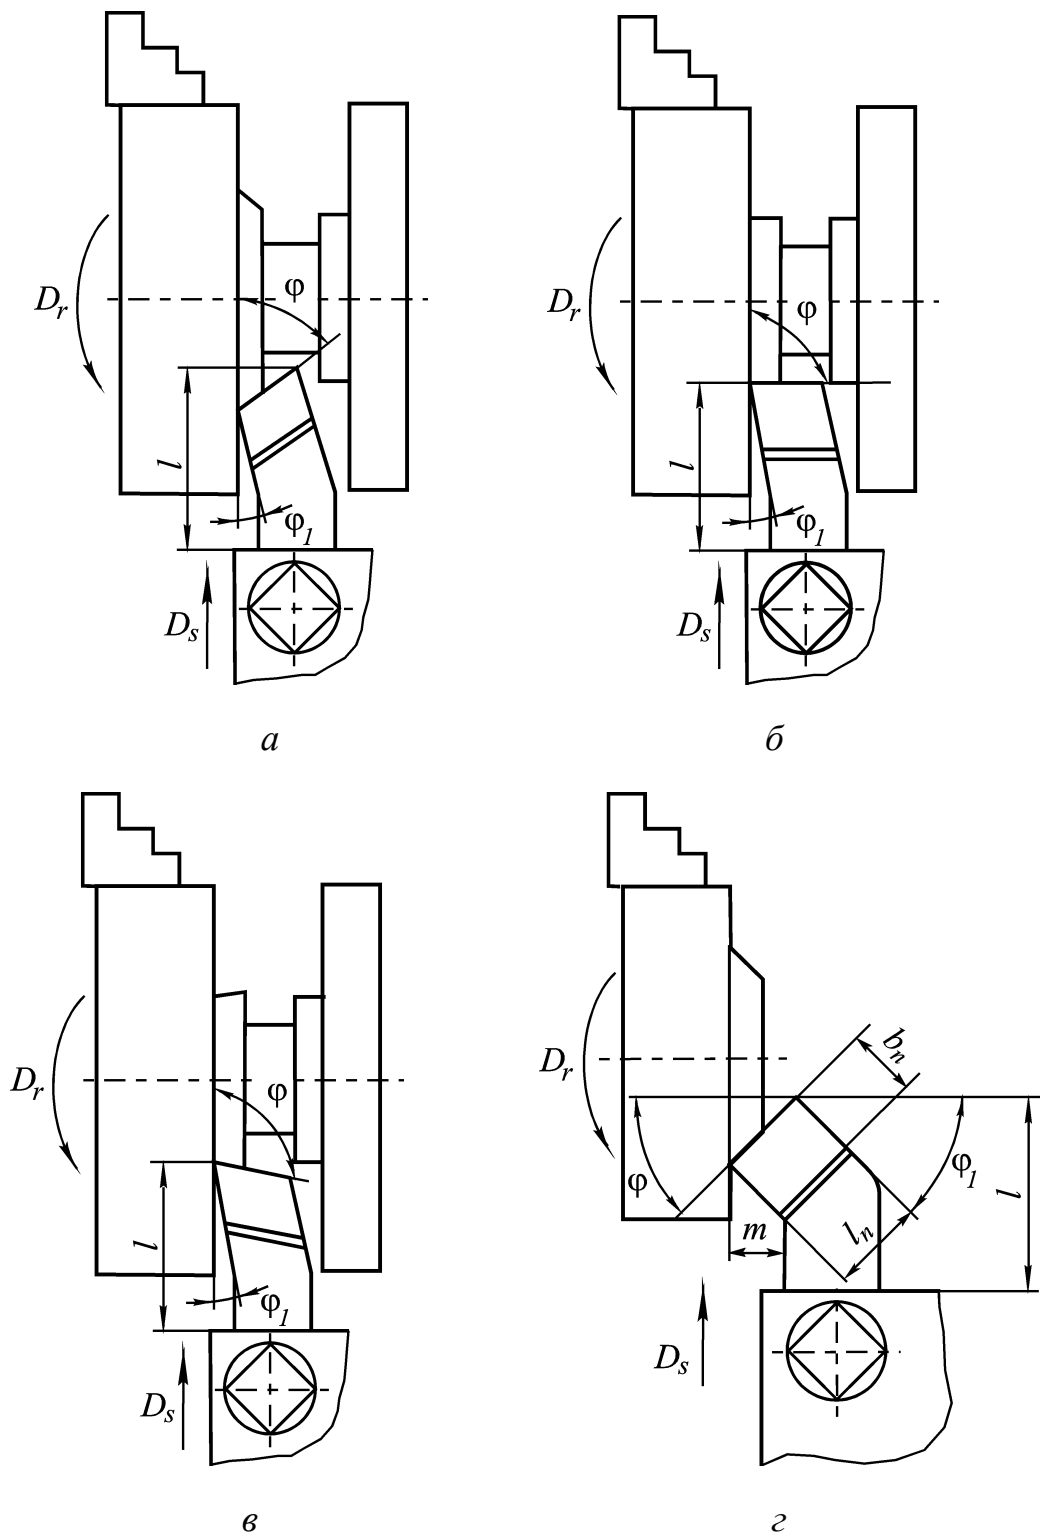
Резцы для обработки торцовых поверхностей [11]:
